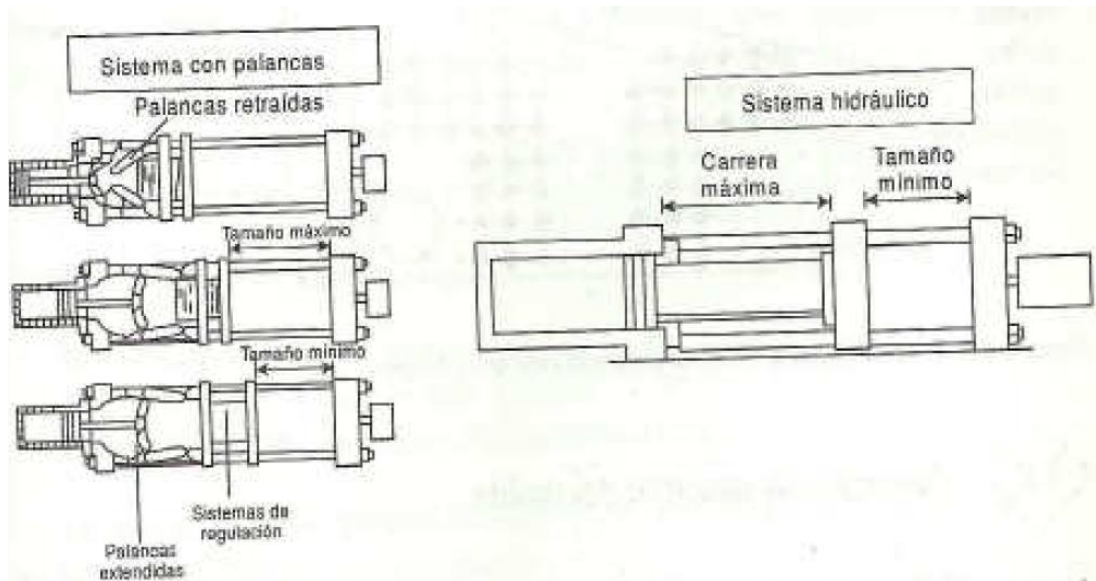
Dimensiones máximas y mínimas de un molde según el sistema de cierre utilizado.
